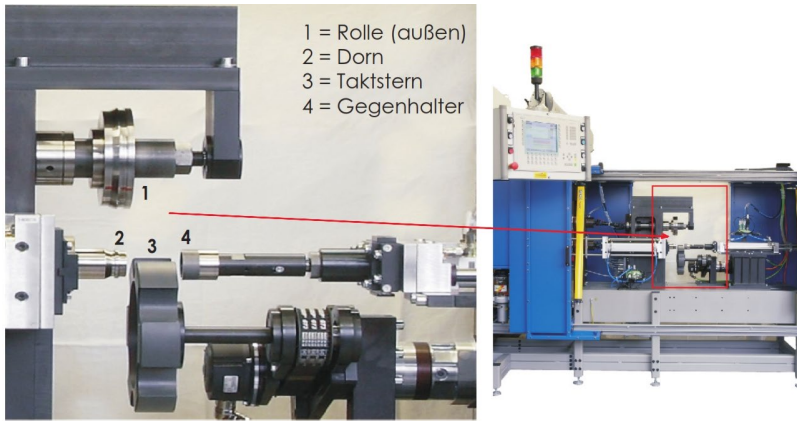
Rollotronic-Maschine und ihr Werkzeugbereich
